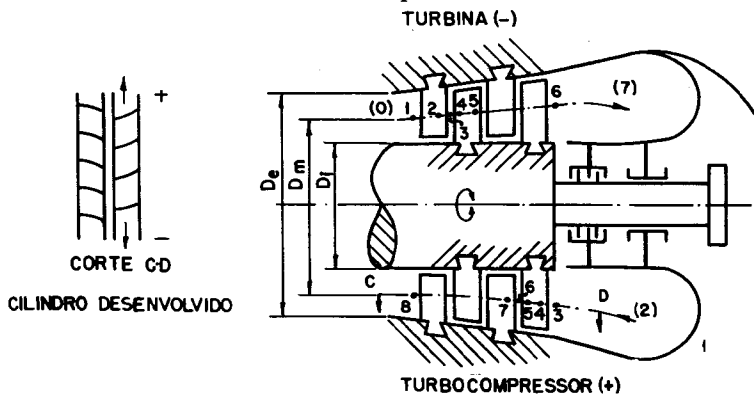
Convenções para turbinas e turbocompressores a gás.
